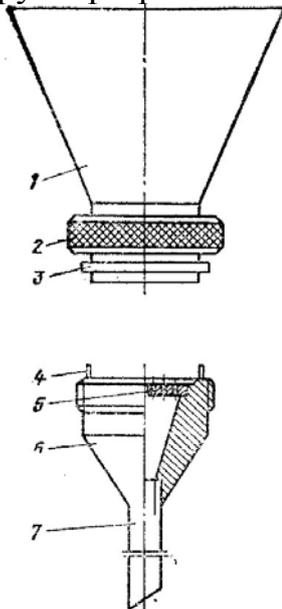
Разъемная воронка: 1 - конус; 2 - накидная гайка; 3 - патрубок; 4 - штифт; 5 - решетка; 6 - штуцер; 7 - трубка
